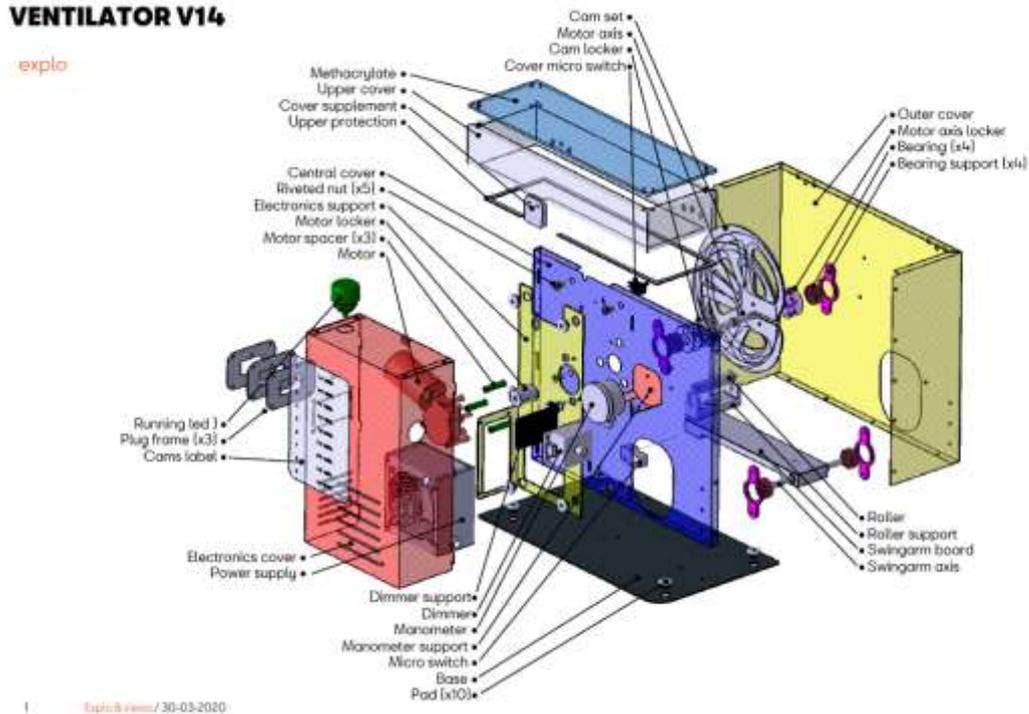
Explosionado OxyGEN-IP. Fuente: Ventilator explo & views, 2020.
